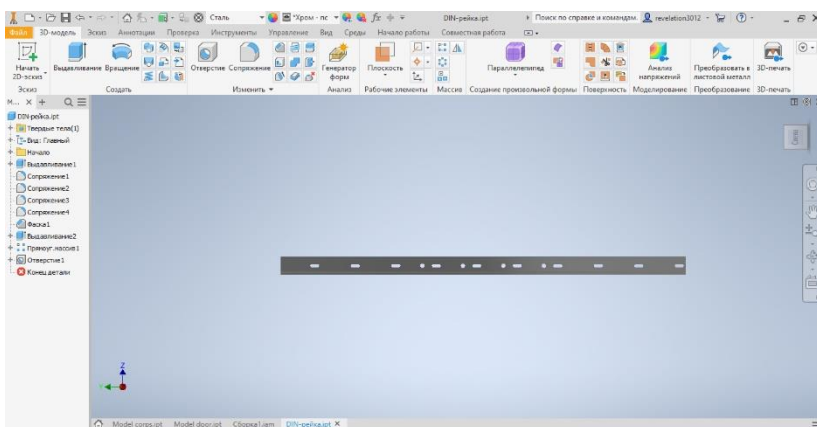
Отримані отвори для болтового з'єднання DIN-рейки
